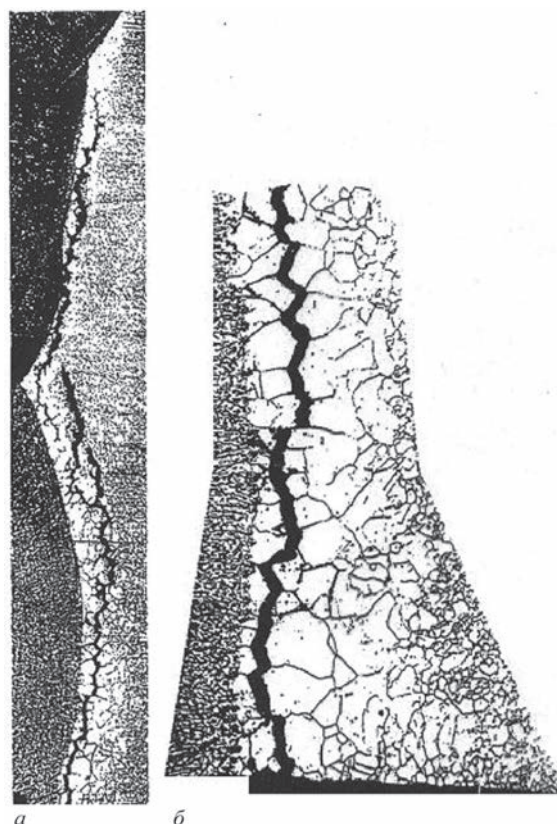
Вигляд тріщини в пришовній зоні зварного з'єднання: а – ×30; б – ×80
